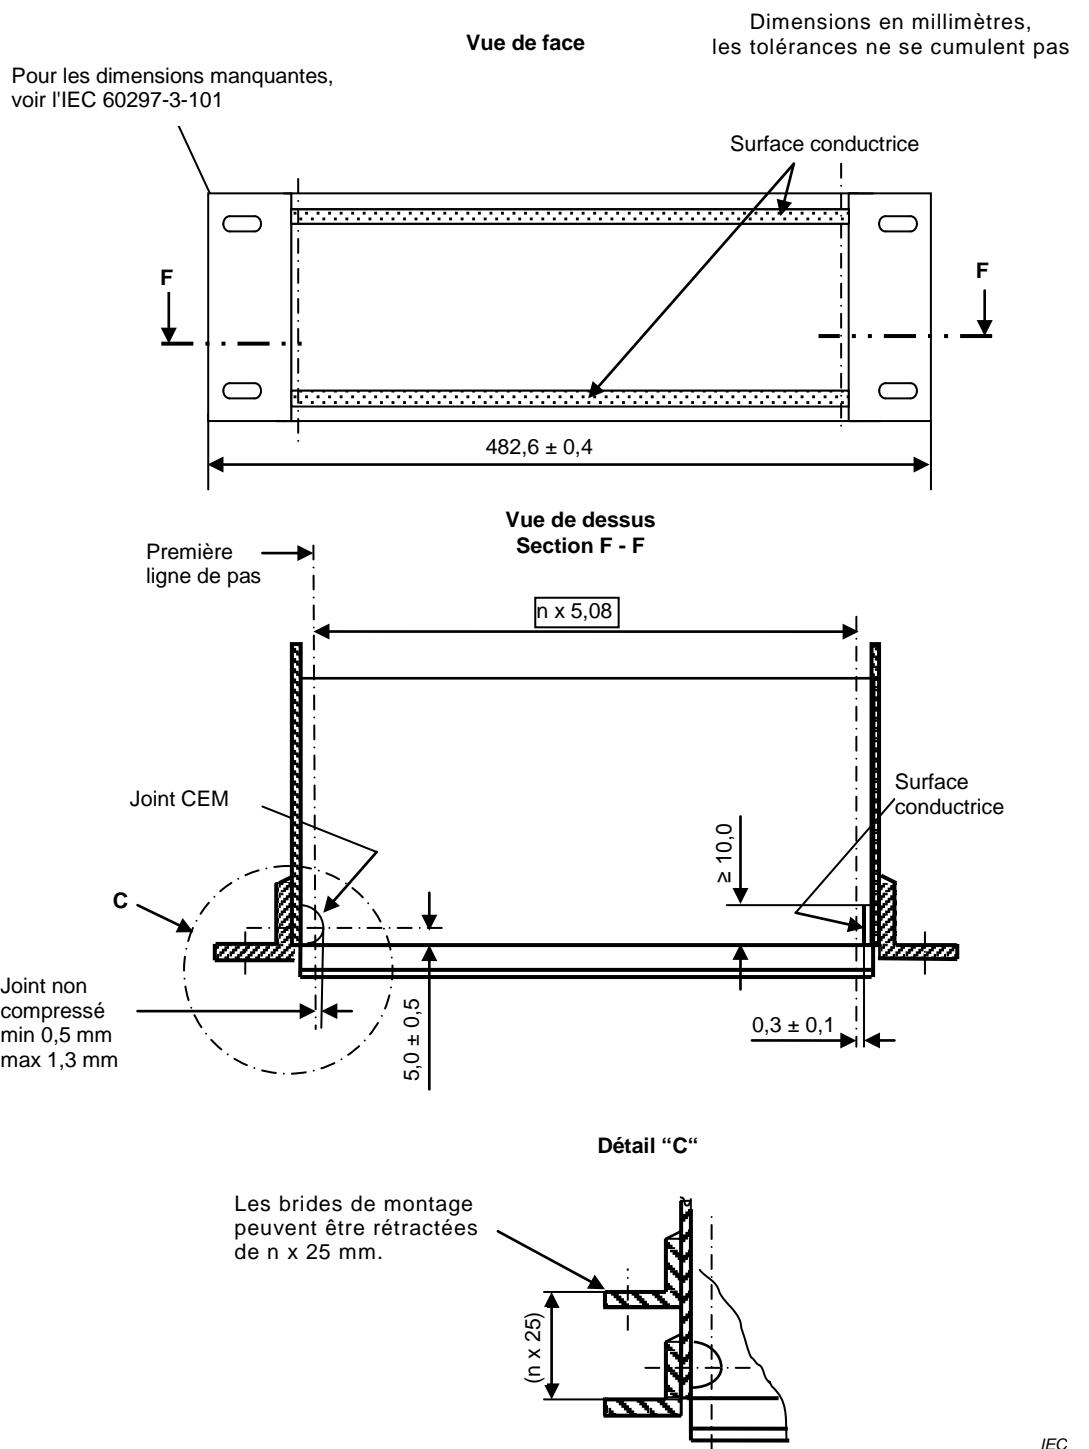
Plan de fixation avant et brides de montage pour un bac de type R
